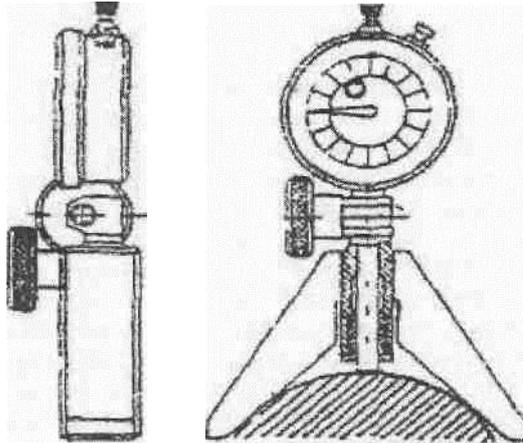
Схема установки индикатора на «О» перед установкой вылета резца по наезднику
